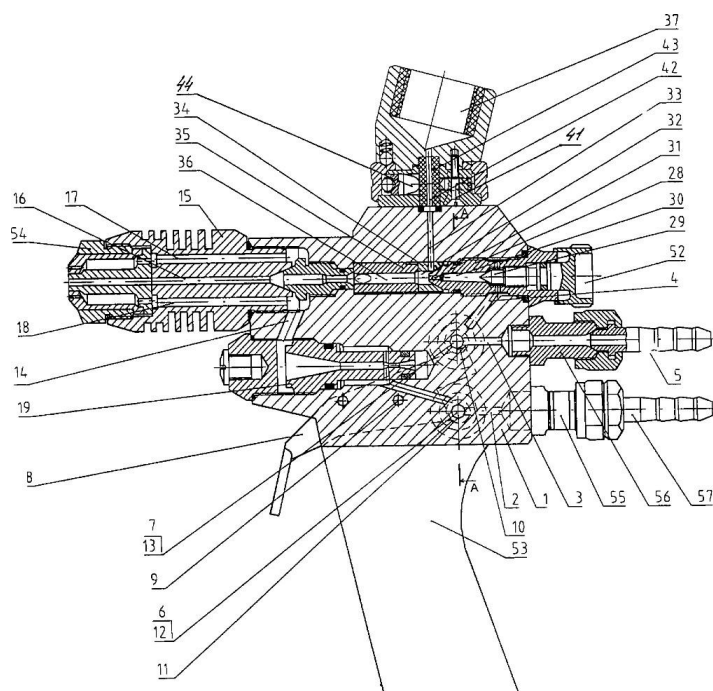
Схема газополум'яного пальника для порошкового наплення «Іскра - 1» (пат. 2211096)
